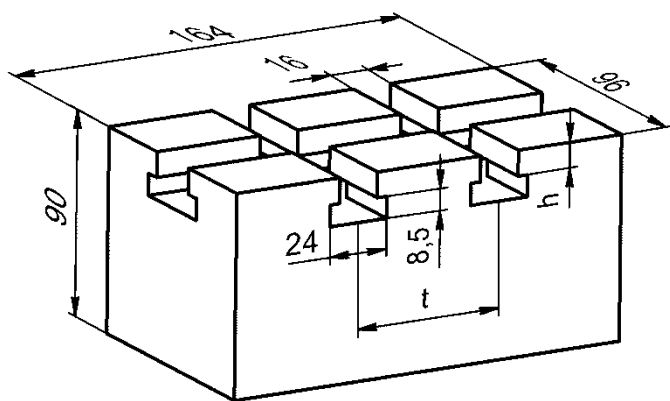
Конструкция и размеры образцов для определения прочности Т-образных пазов в деталях УСРПС
